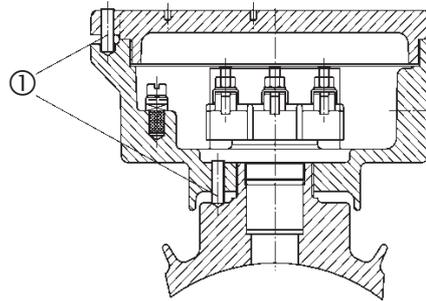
Клеммная коробка с резьбовой шпилькой ①
